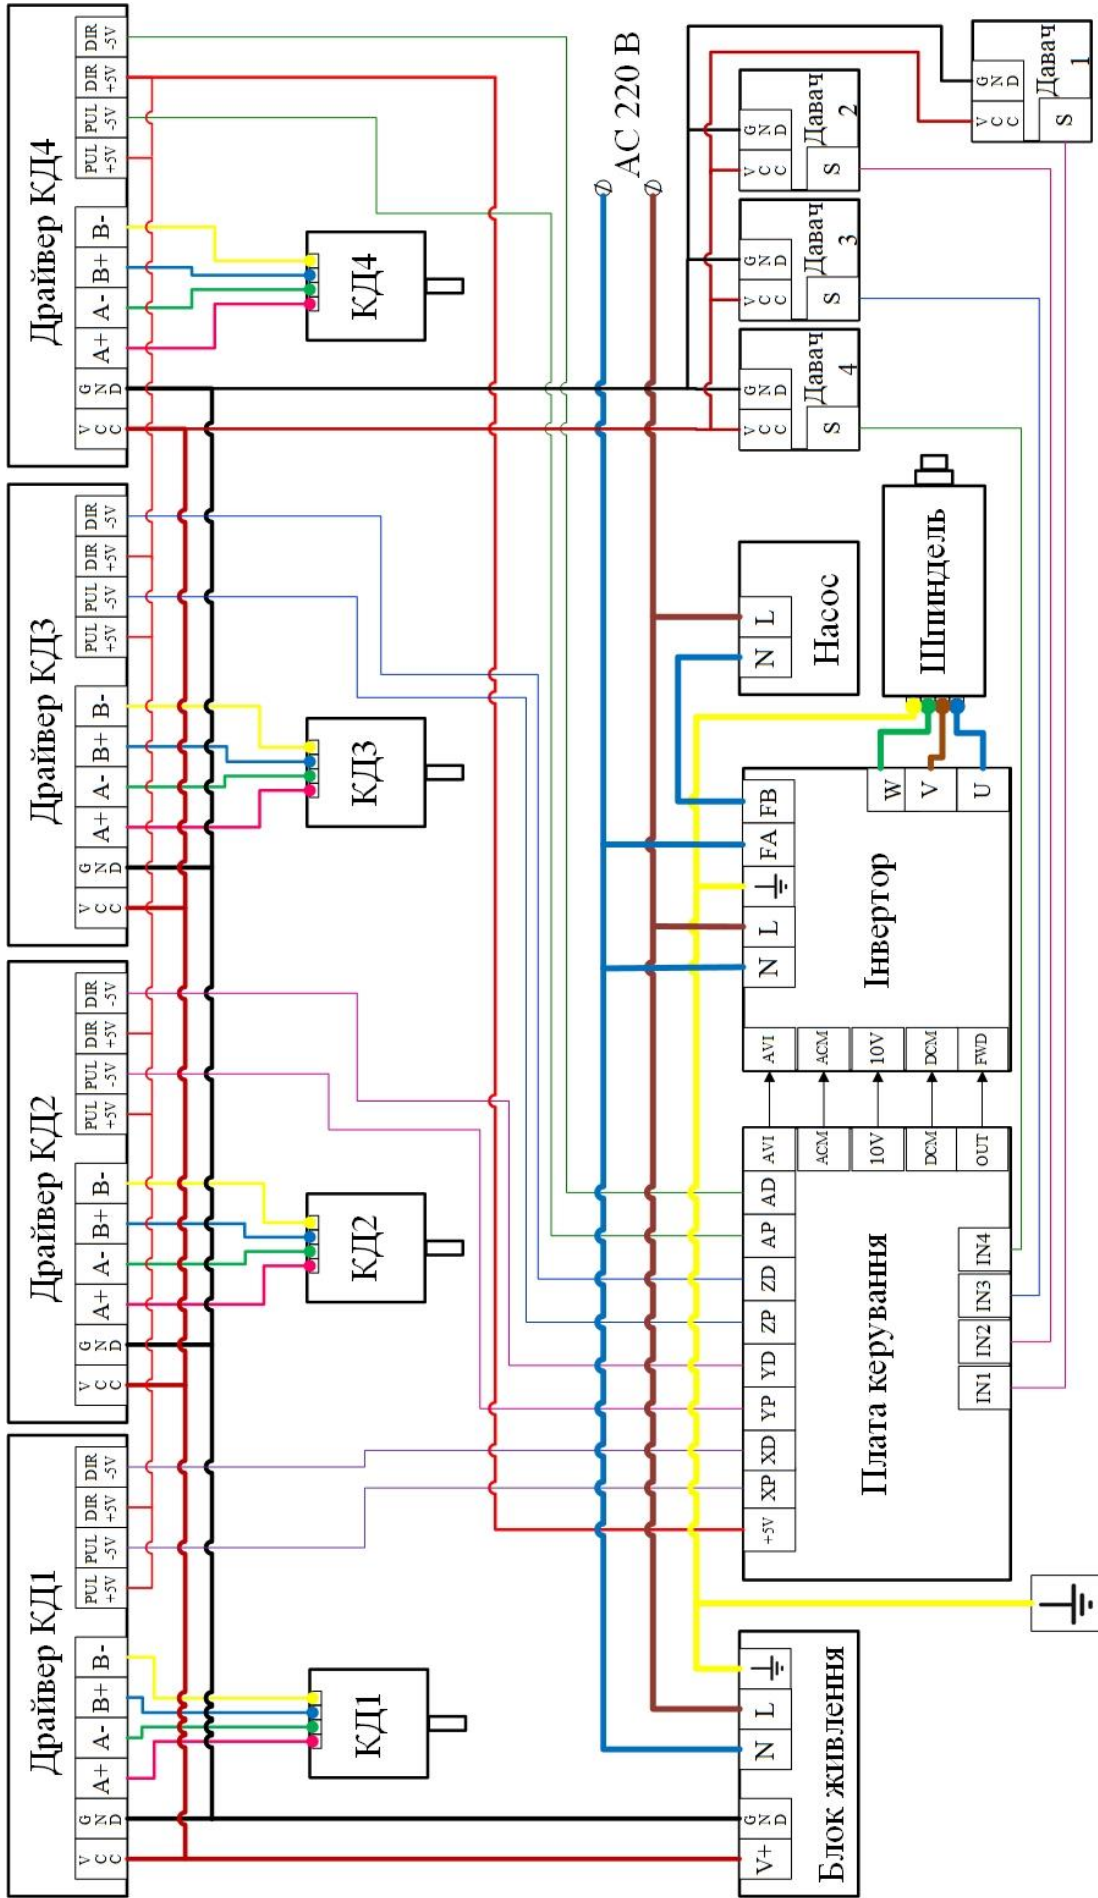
Схема з'єднання електронних компонентів макету фрезерного верстату з ЧПК
